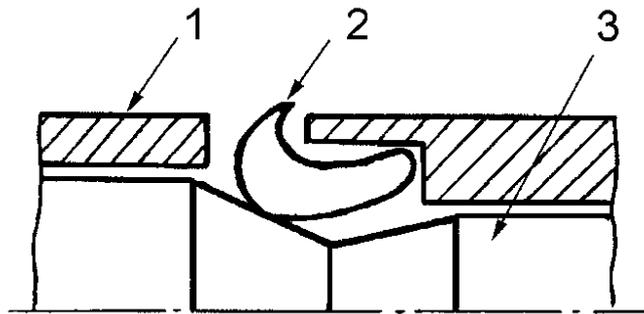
Конструкция крючкового шпалера: 1 — трубка; 2 — крючок (резец); 3 — клин
